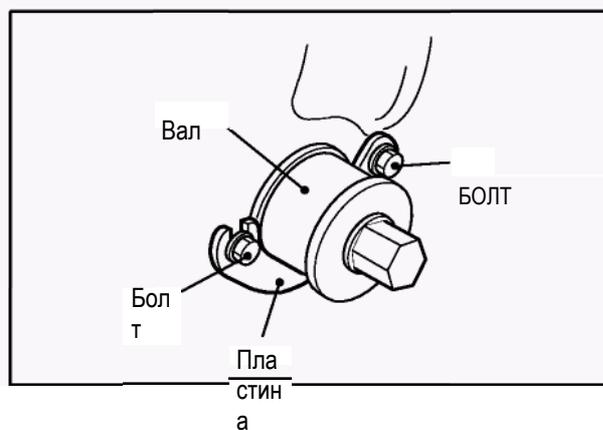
Положение валоповоротного устройства (двигатель работает)
